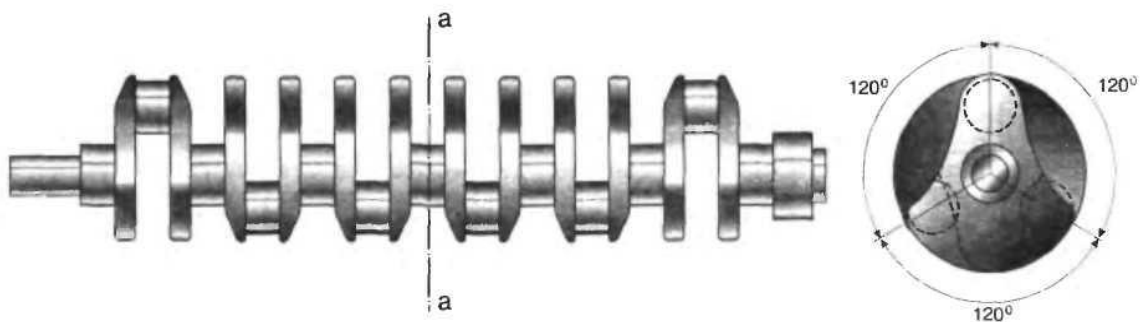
Загальний вигляд типового семиопорного колінчастий валу рядного шестициліндрового двигуна: а-а - площина симетрії
